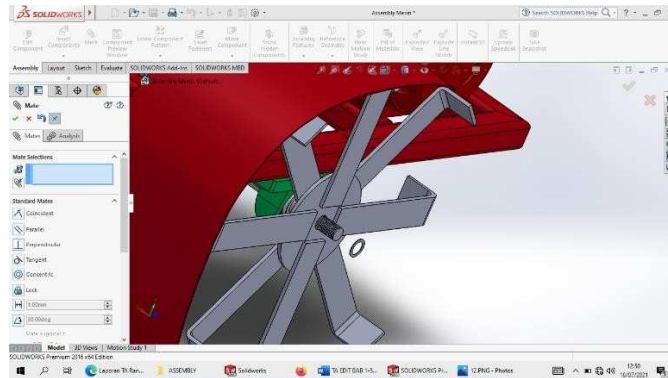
154 Hasil *Assembly* Ring dan Poros Roda
